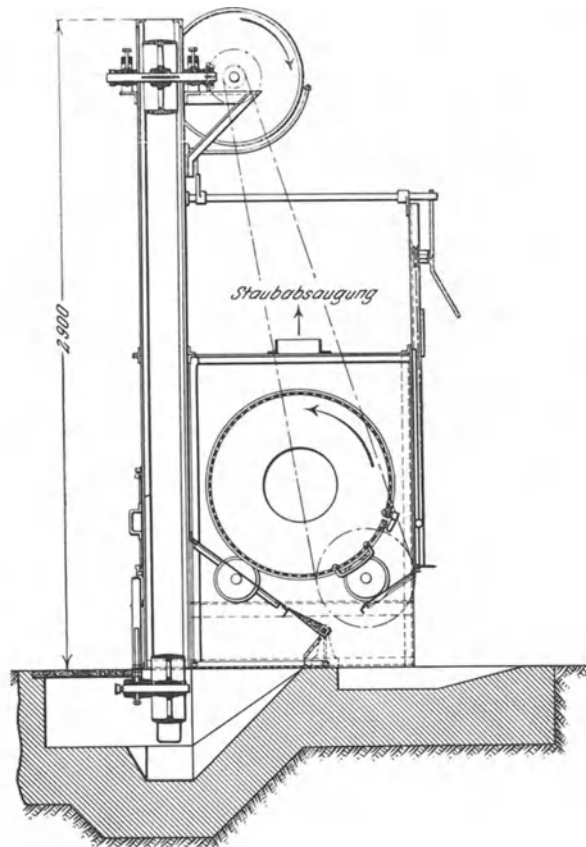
Putztrommel mit Gewindegängen im Innern.
